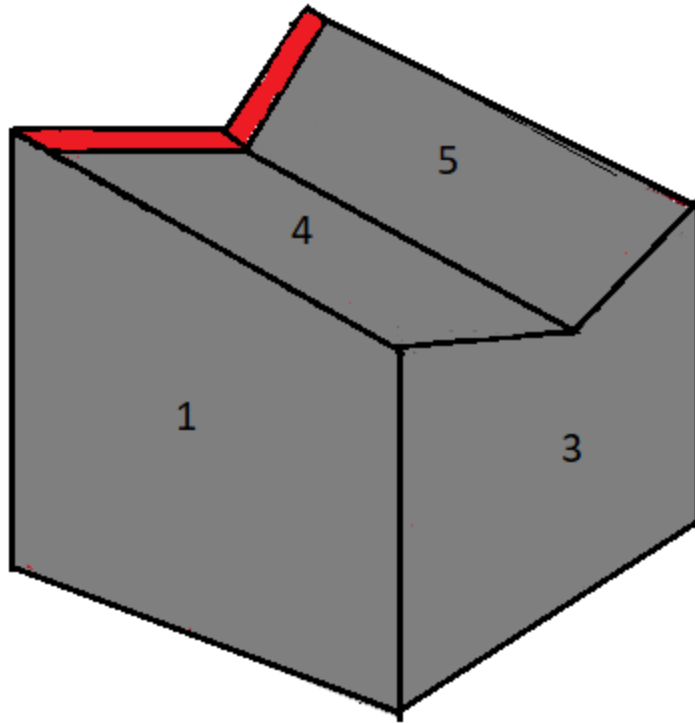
Étape 11 : ajout de pièces optionnelles pour le prototype 3
